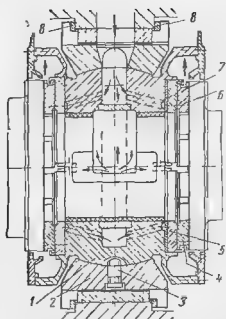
Опорно-упорный подшипник, устанавливаемый между двумя упорными дисками
